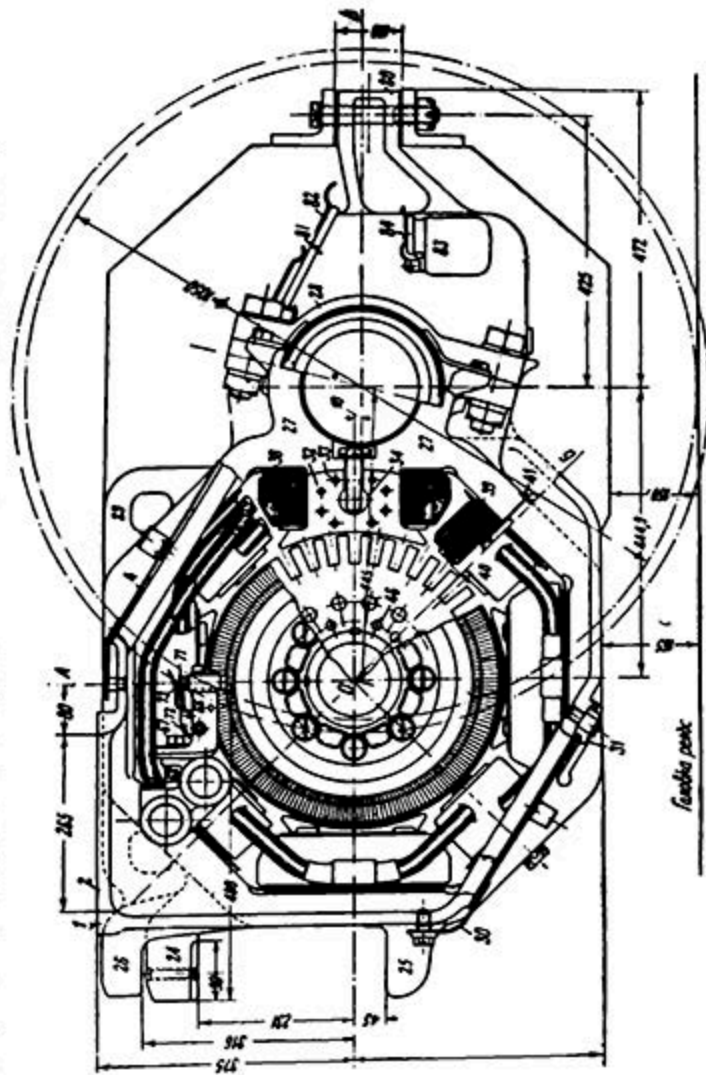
а. Поперечный разрез двигателя ДПИ-150
